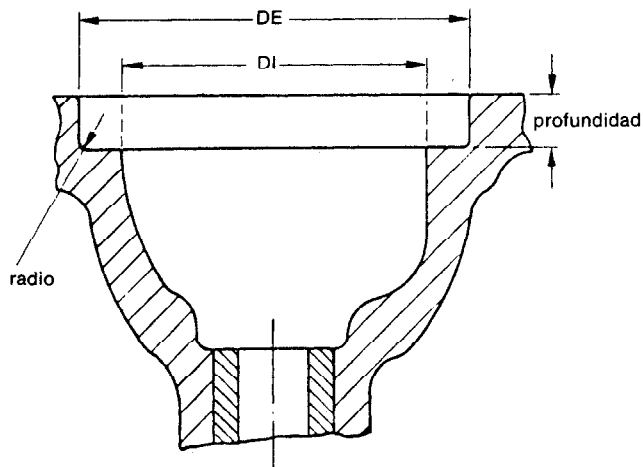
Dimensiones del inserto de asiento de válvula PERKINS
